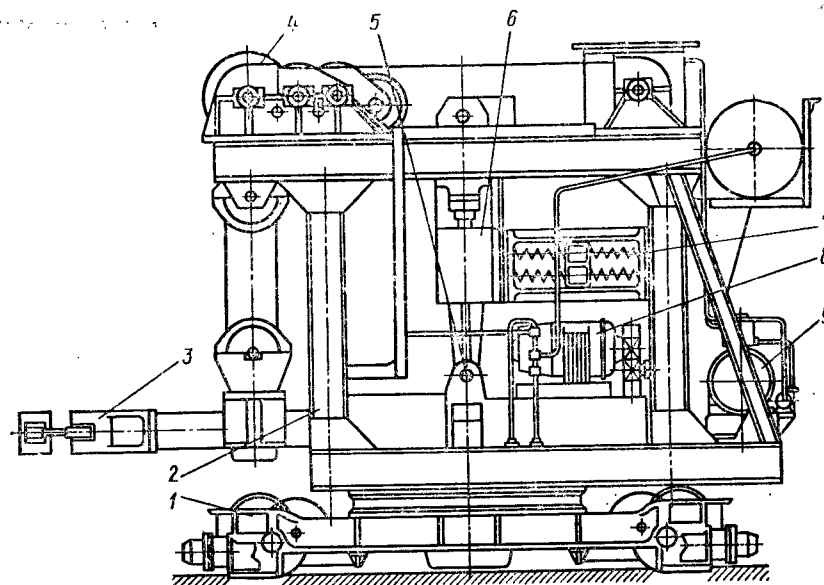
Общий вид напольного полноповоротного кузнечного манипулятора
